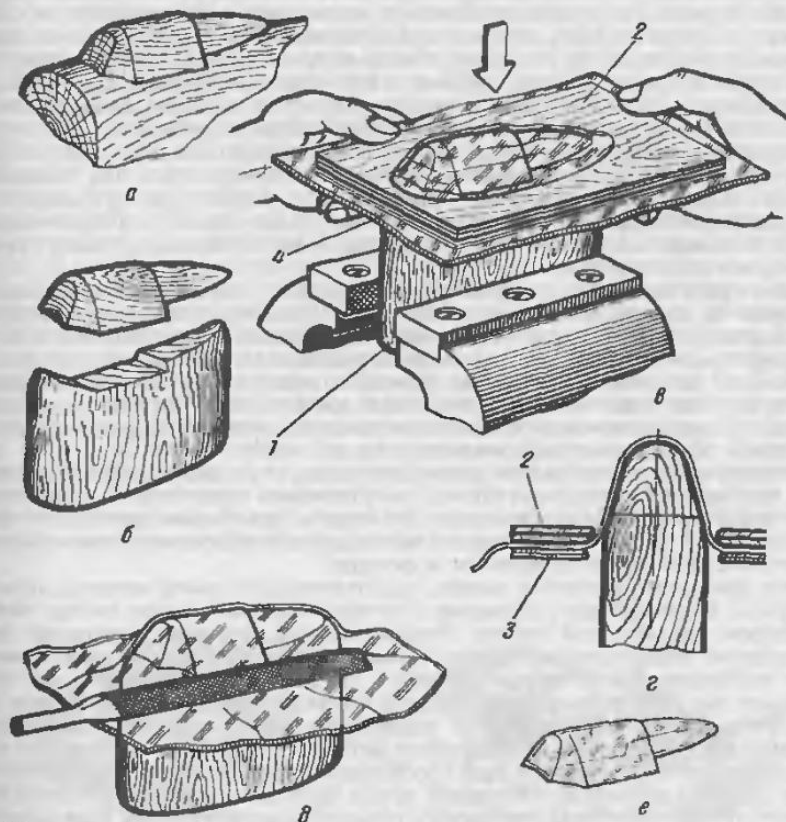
Процесс изготовления (шtamповки) фонаря одноместного самолета-истребителя: а - отрезка заготовки для пуансона; б - изготовление пуансона; в - вытяжка; г - поперечный разрез позиции в; д - обрезка обля; е - готовый фонарь
